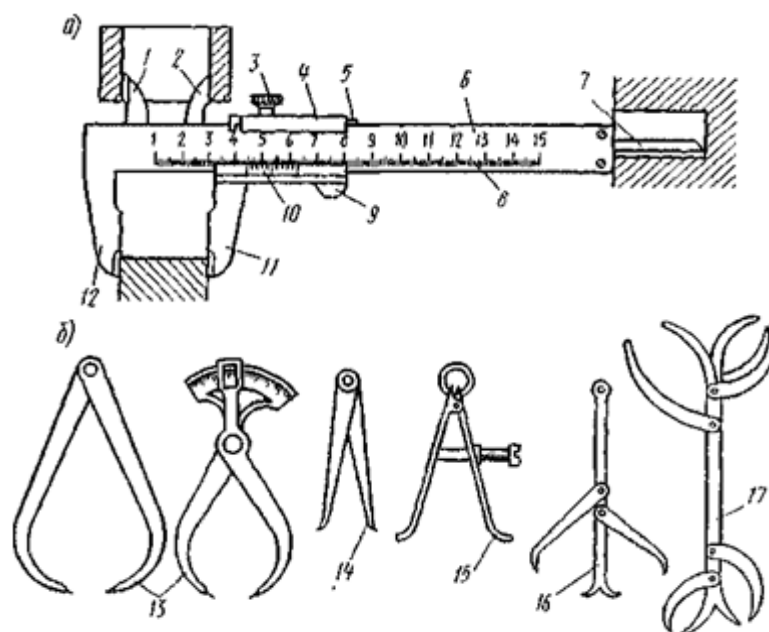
Мерительные инструменты: а – штангенциркуль (1,2 – малые губки для измерения внутренних размеров; 3 – стопорный винт; 4 – подвижная рамка; 5 – пружина; 6 – штанга; 7 – глубиномер; 8 – шкала; 9 – выступ для пальца; 10 – нониусная шкала; 11 – подвижная губка; 12 – неподвижная губка); б – кронциркули 13, нутромеры 14, 15, комбинированный мерительный инструмент 16, 17
